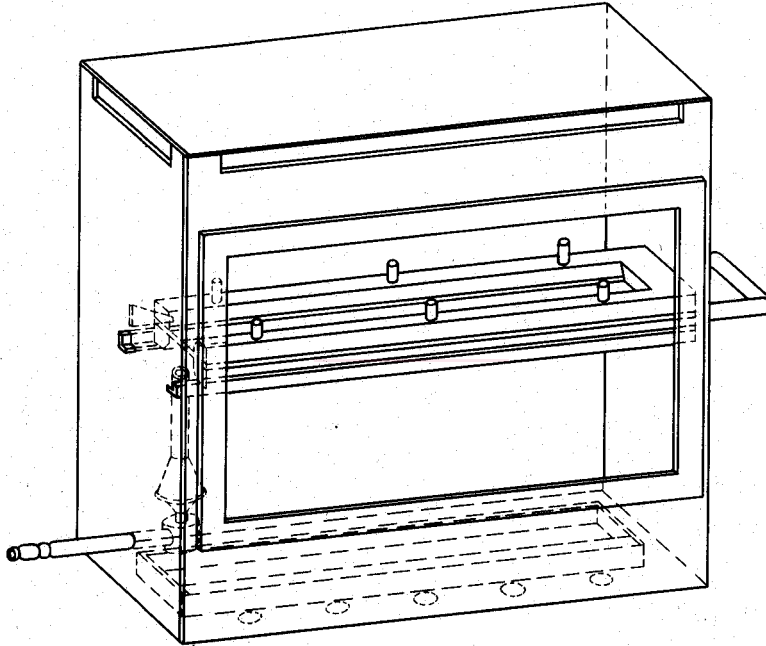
Exemple de chambre de combustion, avec porte-échantillon et cuvette
